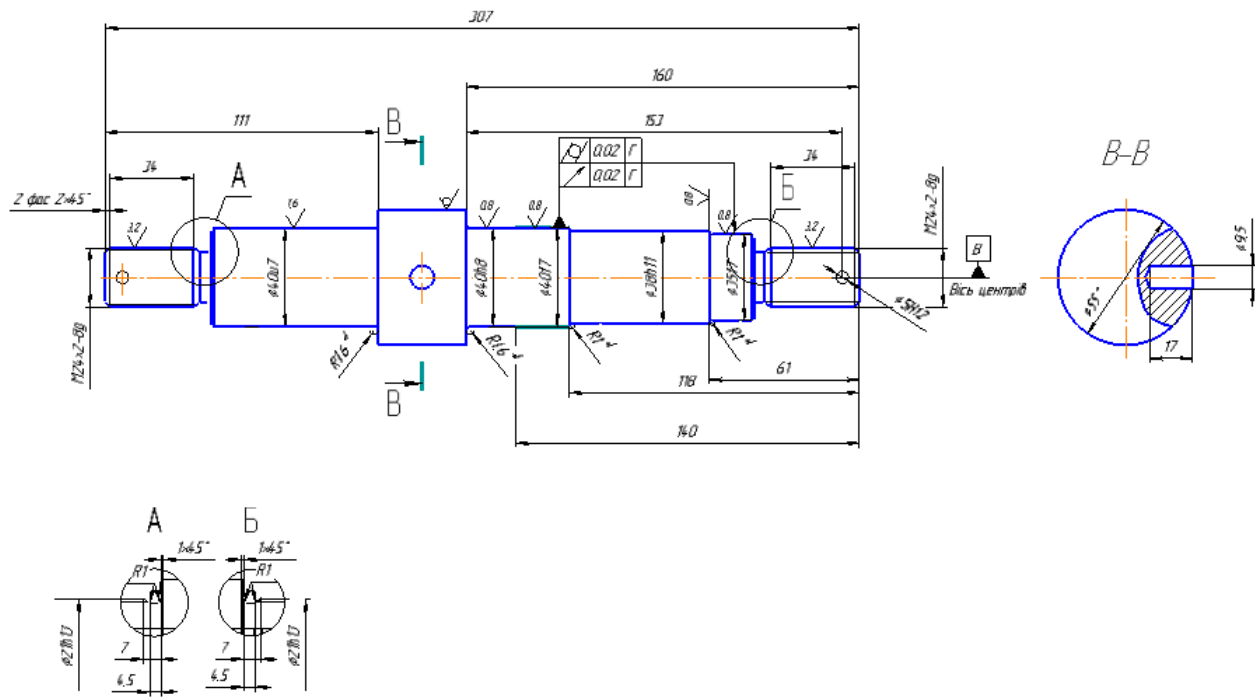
Робоче креслення вісі котка танку Т-72.
